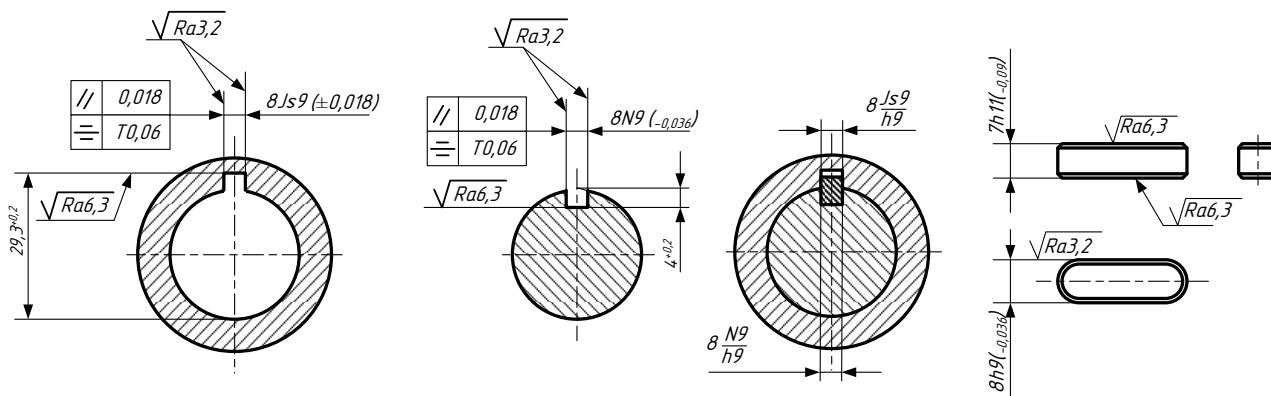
Эскизы шпоночного соединения и деталей
